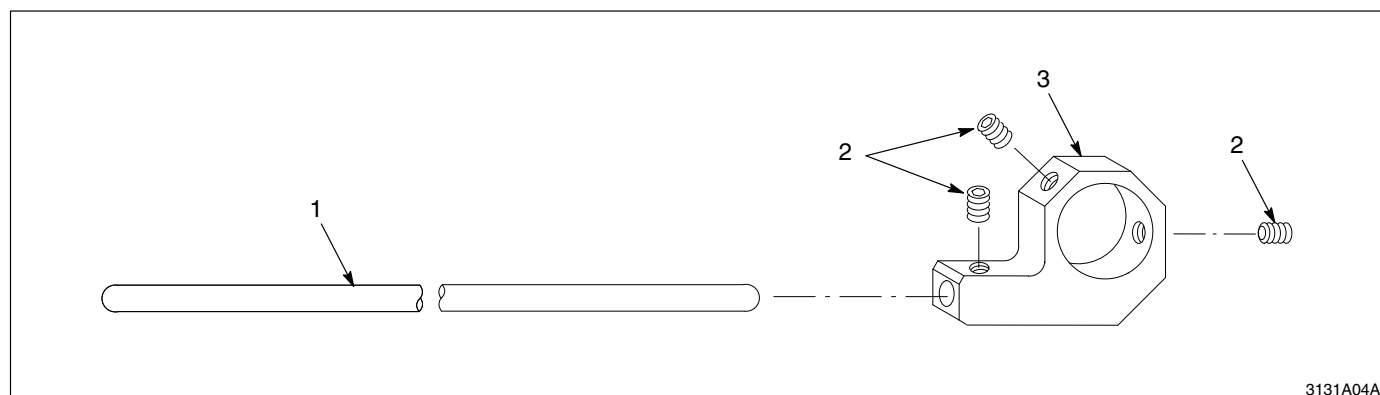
Bausatz Ionenkollector für Shur-Lok Halterung
